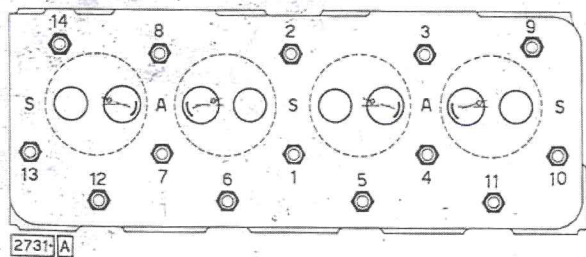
Schema di montaggio delle valvole di aspirazione (A) e di scarico (S) e ordine di serraggio dei dadi per prigionieri di fissaggio testa cilindri al basamento motore.
